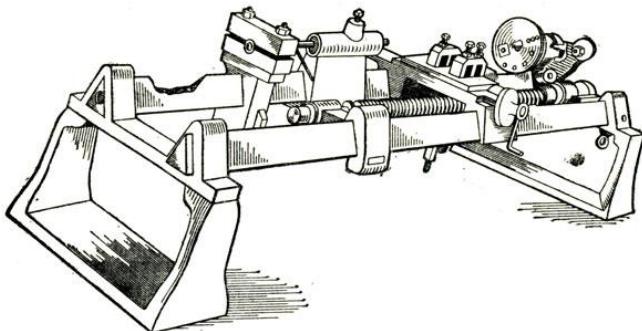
Токарно-винторезный станок Генри Модсли
